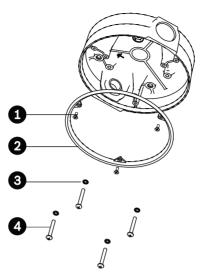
Colocação da junta circular e do anel de retenção para instalação exterior
